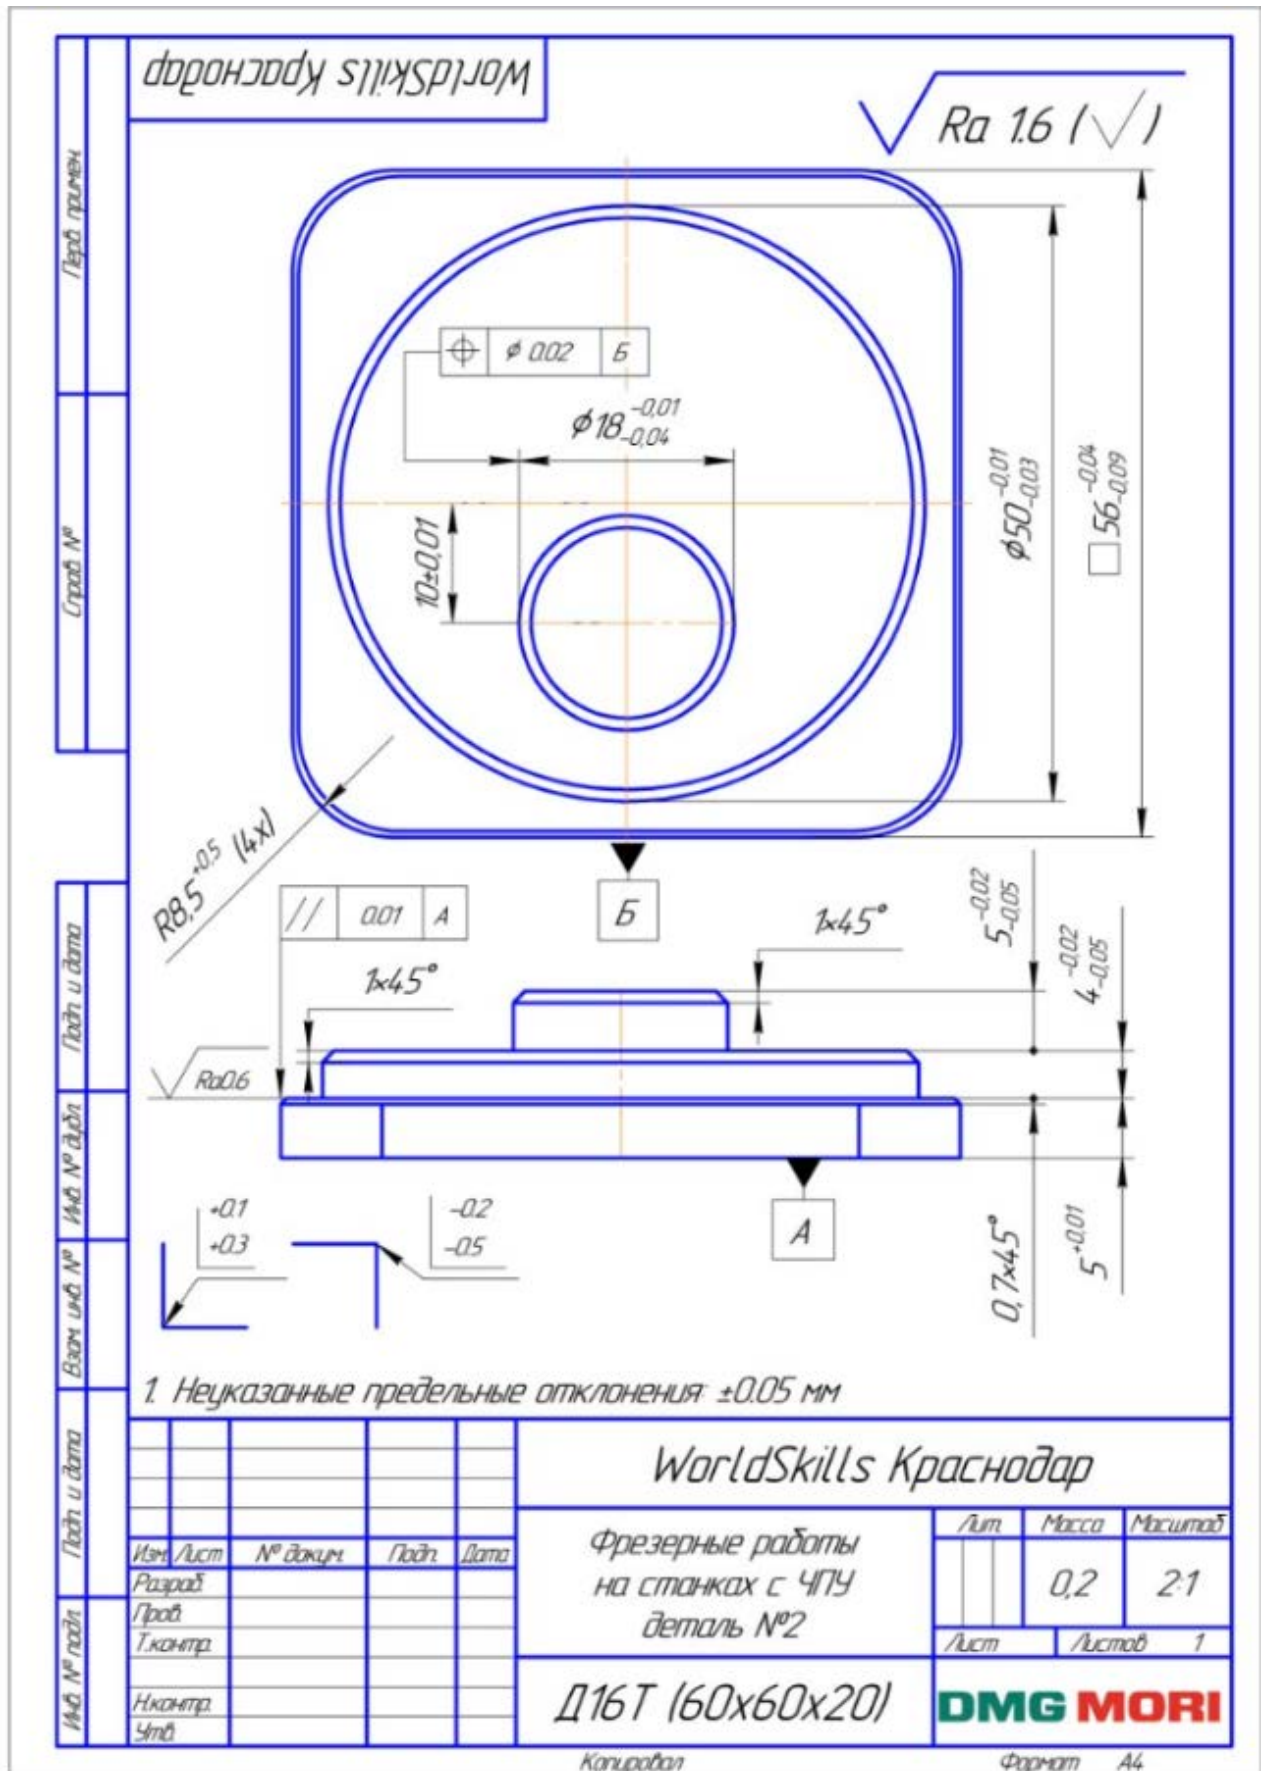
Деталь 2 Фрезерные работы на станках с ЧПУ
